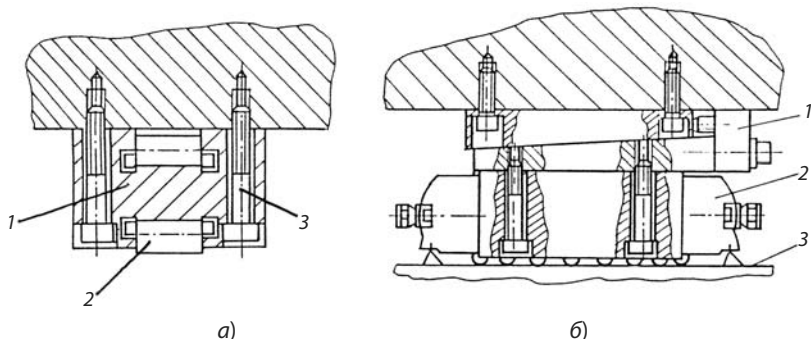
Роликовая опора (танкетка), способ ее крепления и создания предварительного натяга:
